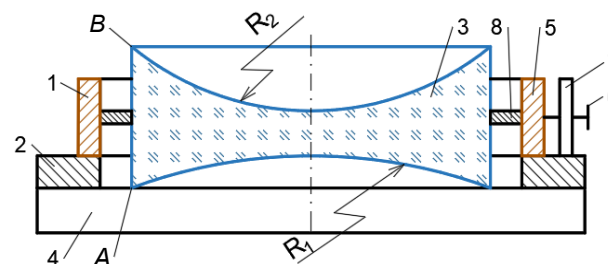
Схема устройства для крепления линзы за боковую поверхность
